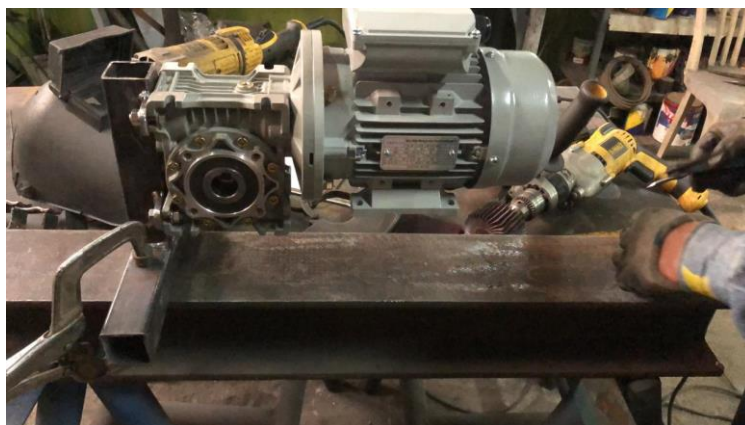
Soportes para el motorreductor y motor. Fuente: Autor
